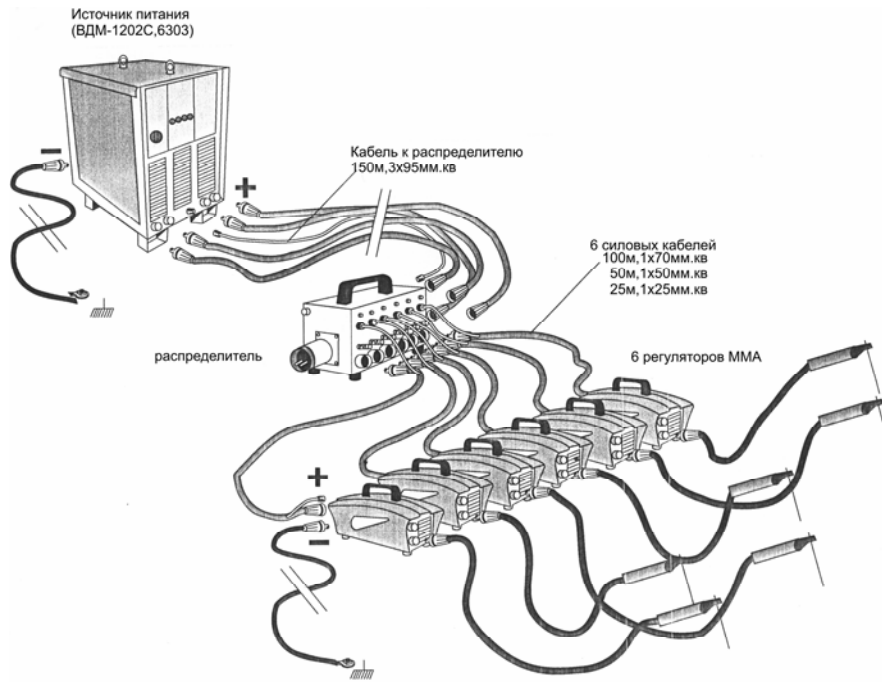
Вариант применения КСУ-320 для ручной дуговой сварки.
